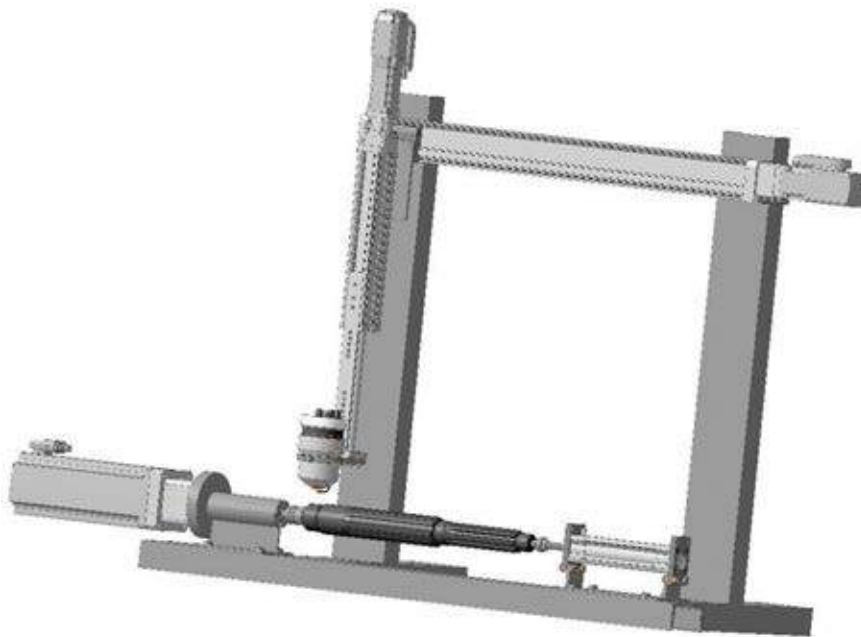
Установка з ЧПК для автоматизованого відновлення деталей типу «вал»
